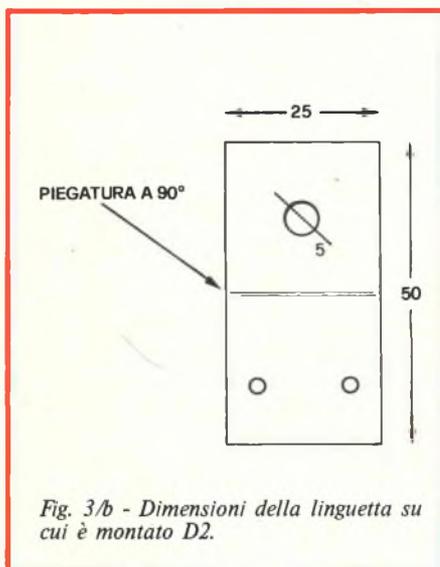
/b - Dimensioni della linguetta su cui è montato D2.
